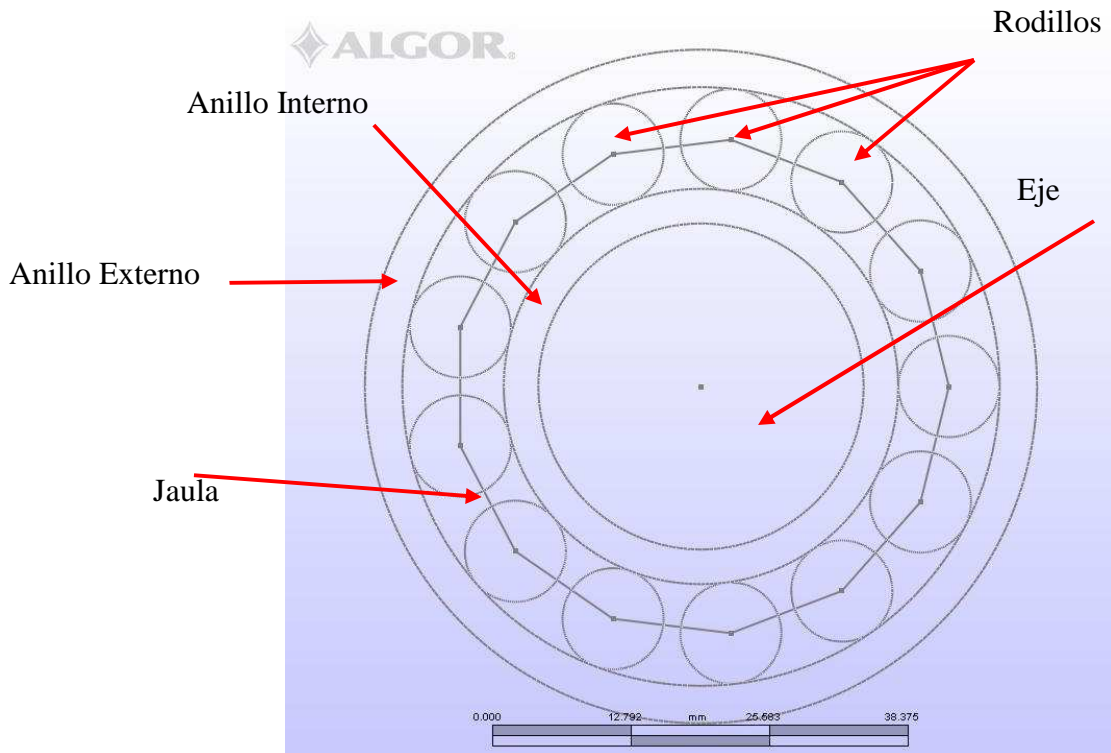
Esquema del modelo de rodamiento de rodillos bajo FEM/MES.
